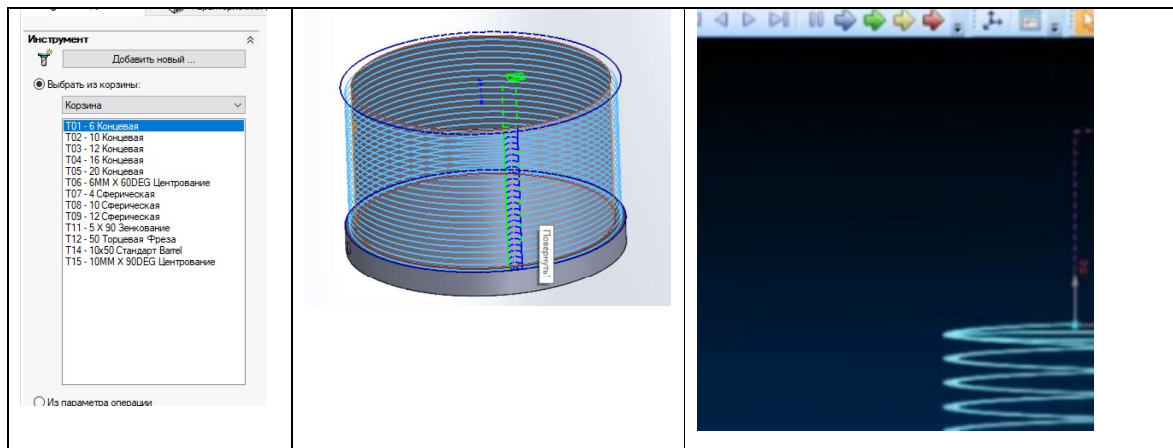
Траєкторія вершини ріжучого інструменту при фрезеруванні циліндричної поверхні та профілю внутрішньої різьби
